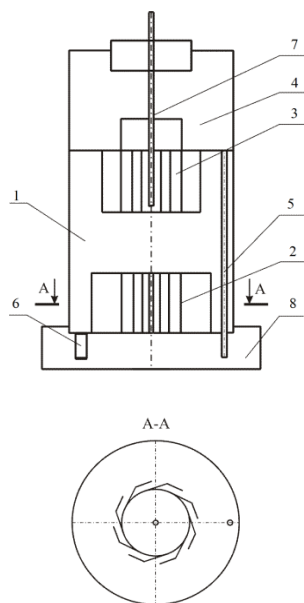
Вихревой пылеулавливающий элемент: 1 - корпус; 2 - завихритель нижний; 3 - завихритель верхний; 4 - сепаратор; 5, 6 - патрубок слива; 7 - патрубок ввода воды; 8 - тарелка
